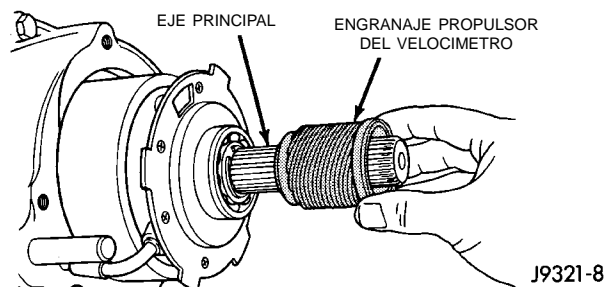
Desmontaje del engranaje propulsor del velocímetro
